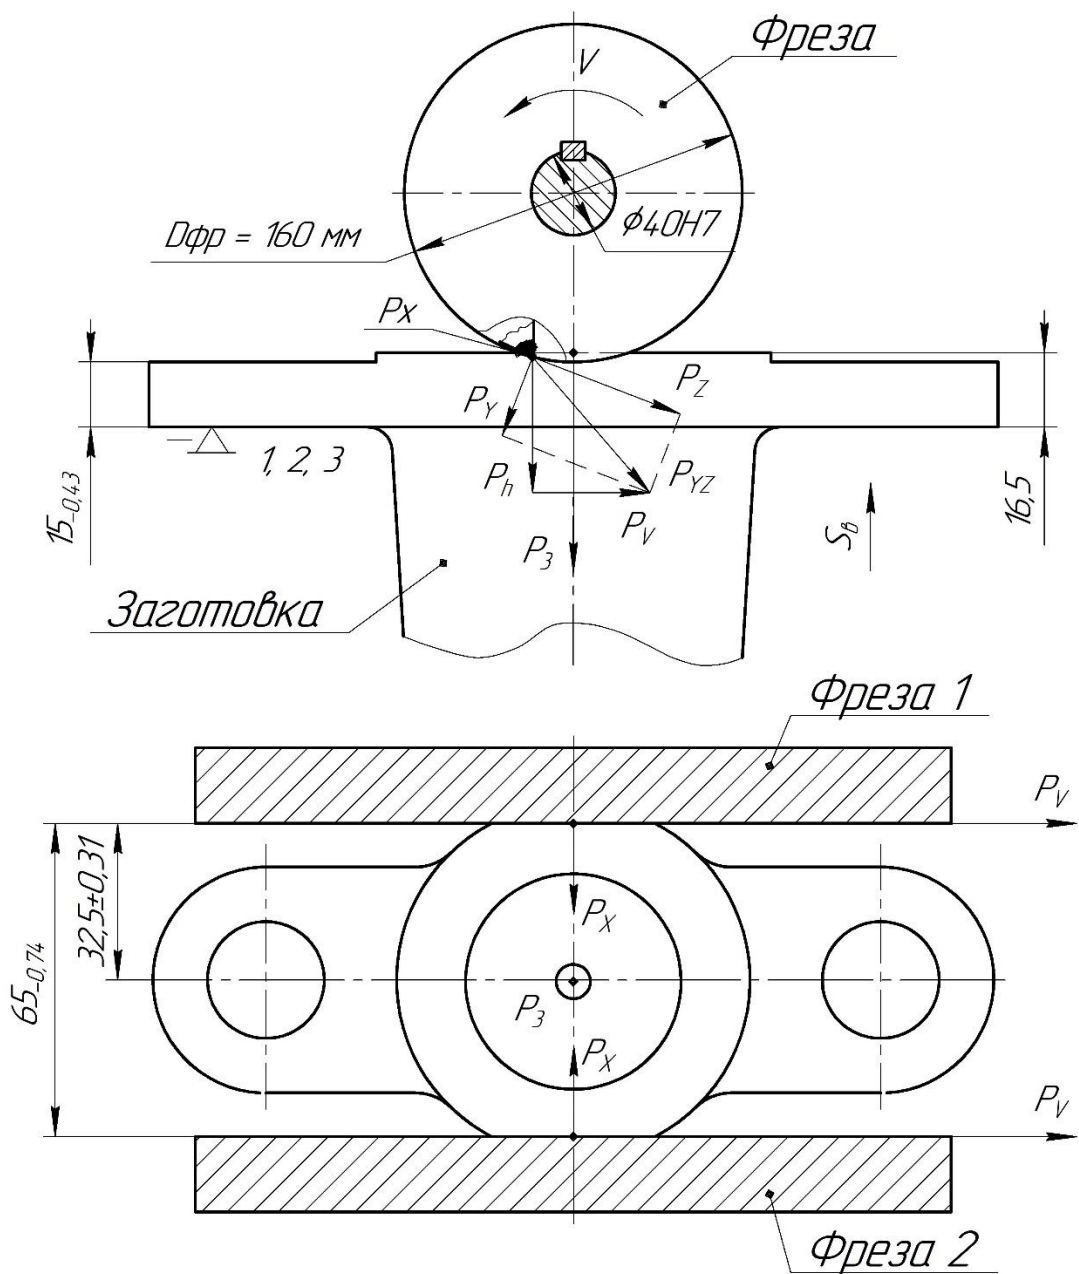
Схема для розрахунку сили закріплення заготовки
